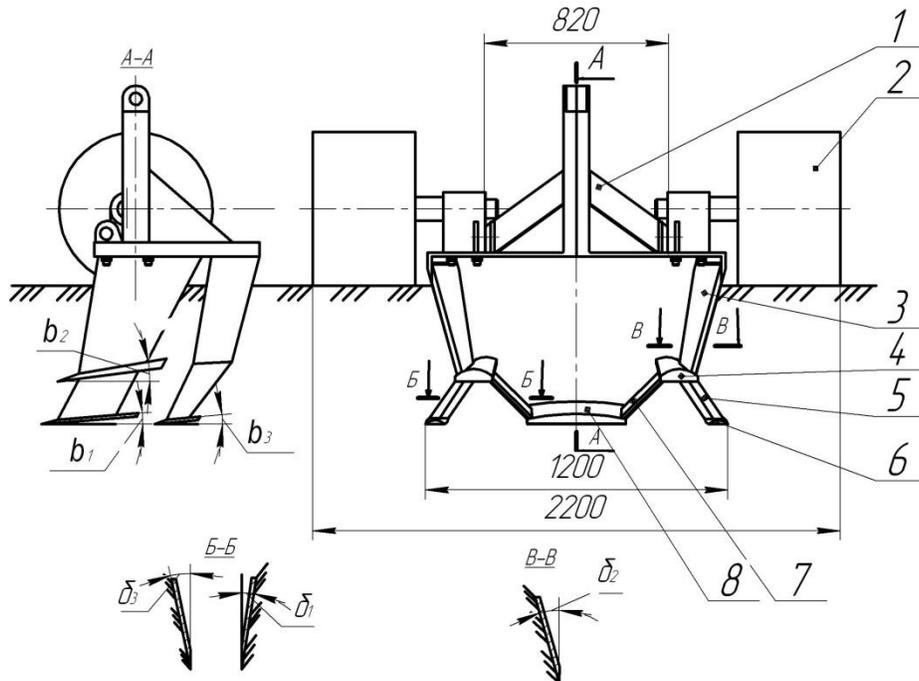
Двухступенчатый двухрядный глубокорыхлитель РГ-0.5.2.
